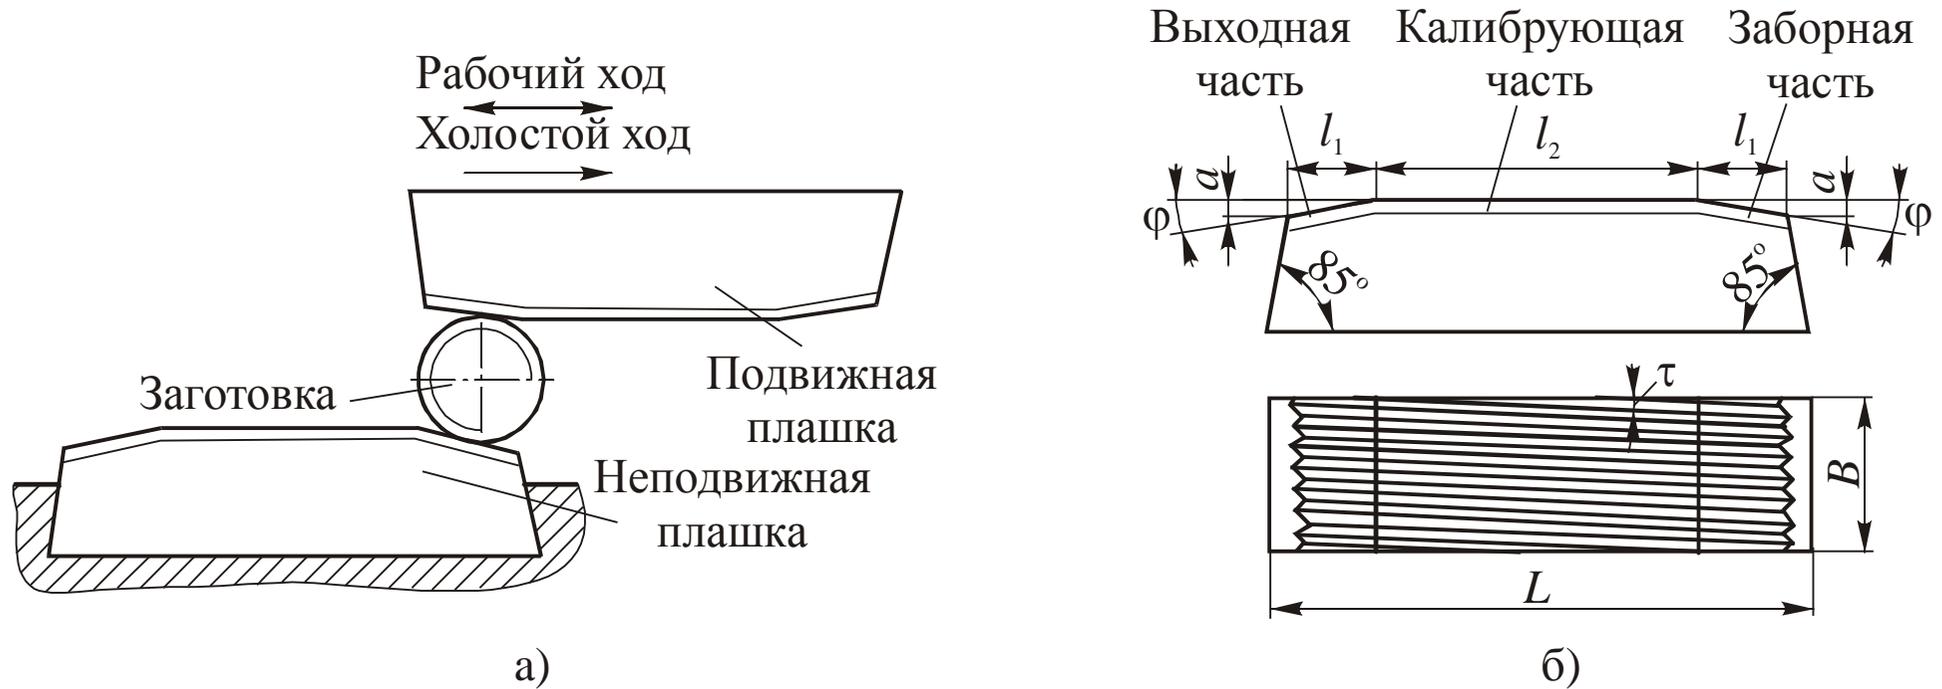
Накатывание резьбы плоскими плашками: а – схема накатывания; б – элементы резьбы на неподвижной плашке
